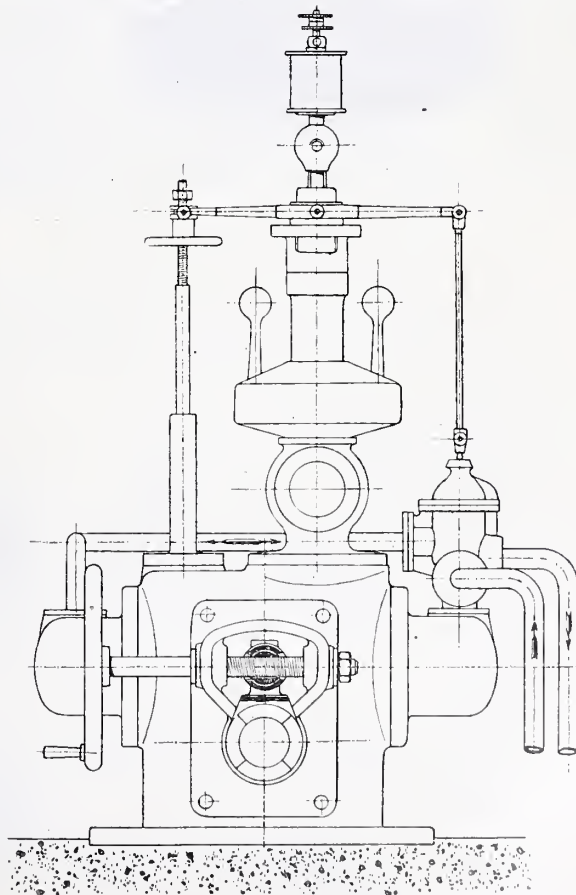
Schema des Regulators mit hydraulischem Hochdruck-Servomotor. Ansicht.
